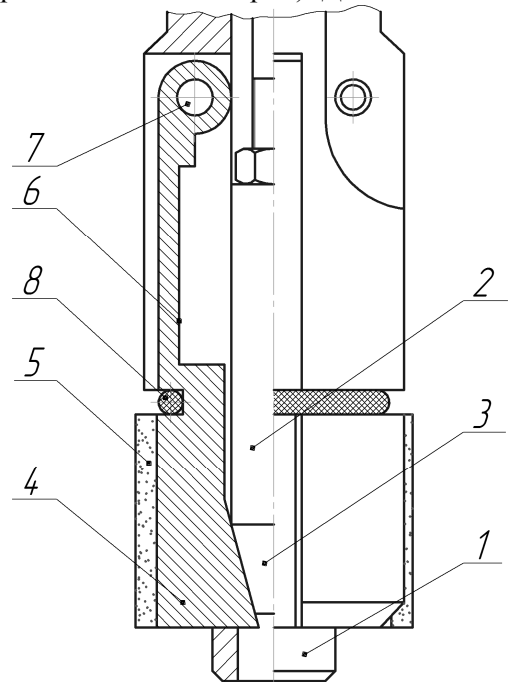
Схема конструкции инструмента с фиксированными осями поворота режущих элементов
